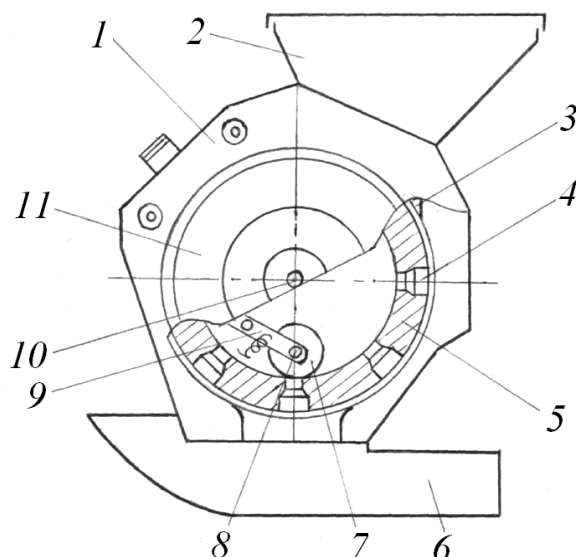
Висівний апарат: 1 – корпус; 2 – бункер; 3 – камера забору; 4 – комірка; 5 – висівний диск; 6 – сошник; 7 – ролик; 8 – вісь; 9 – вилка; 10 – вал; 11 – кришка.
